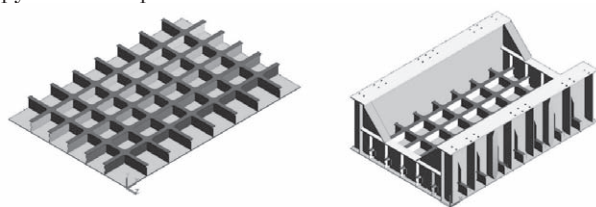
Базовый вариант исполнения конструкции ледовой защиты
